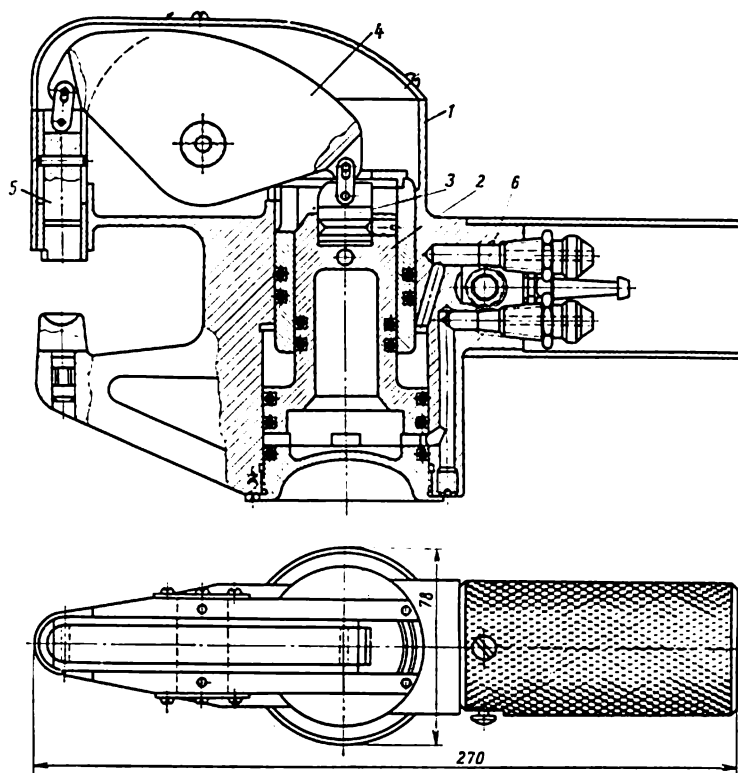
Presse oléopneumatique portable pour l'assemblage des tôles minces:
